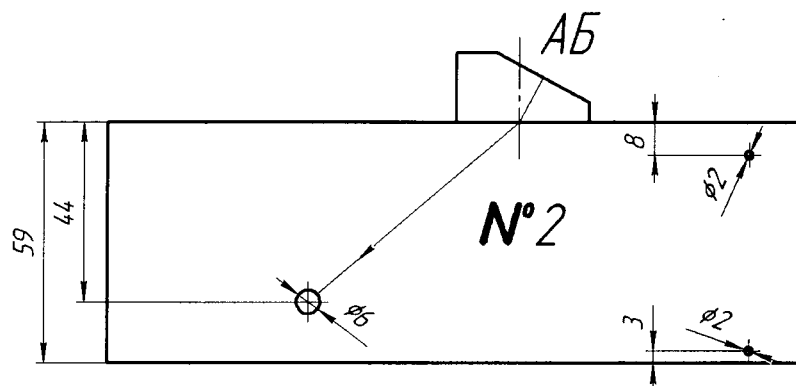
Установка акустического блока на поверхность контрольного образца №2 для получения сигнала от бокового сверления диаметром 6 мм.
